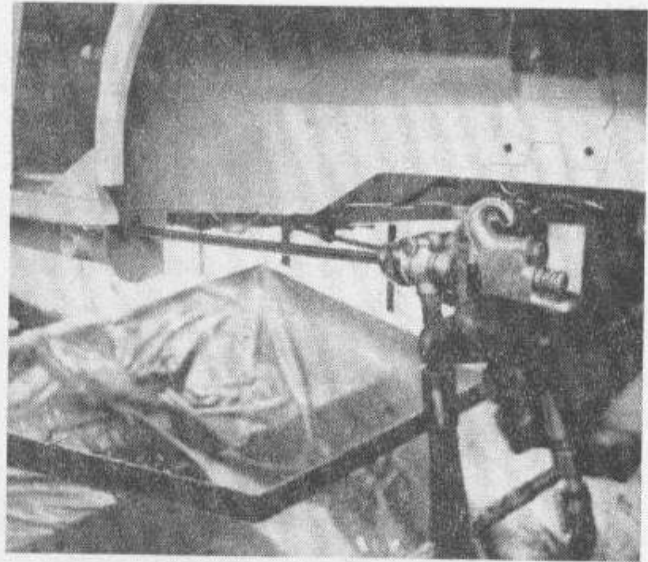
Das Aussprühen der Längsträger des Trabant mit Bitumen erfolgt mittels einer Langrohrpistole
